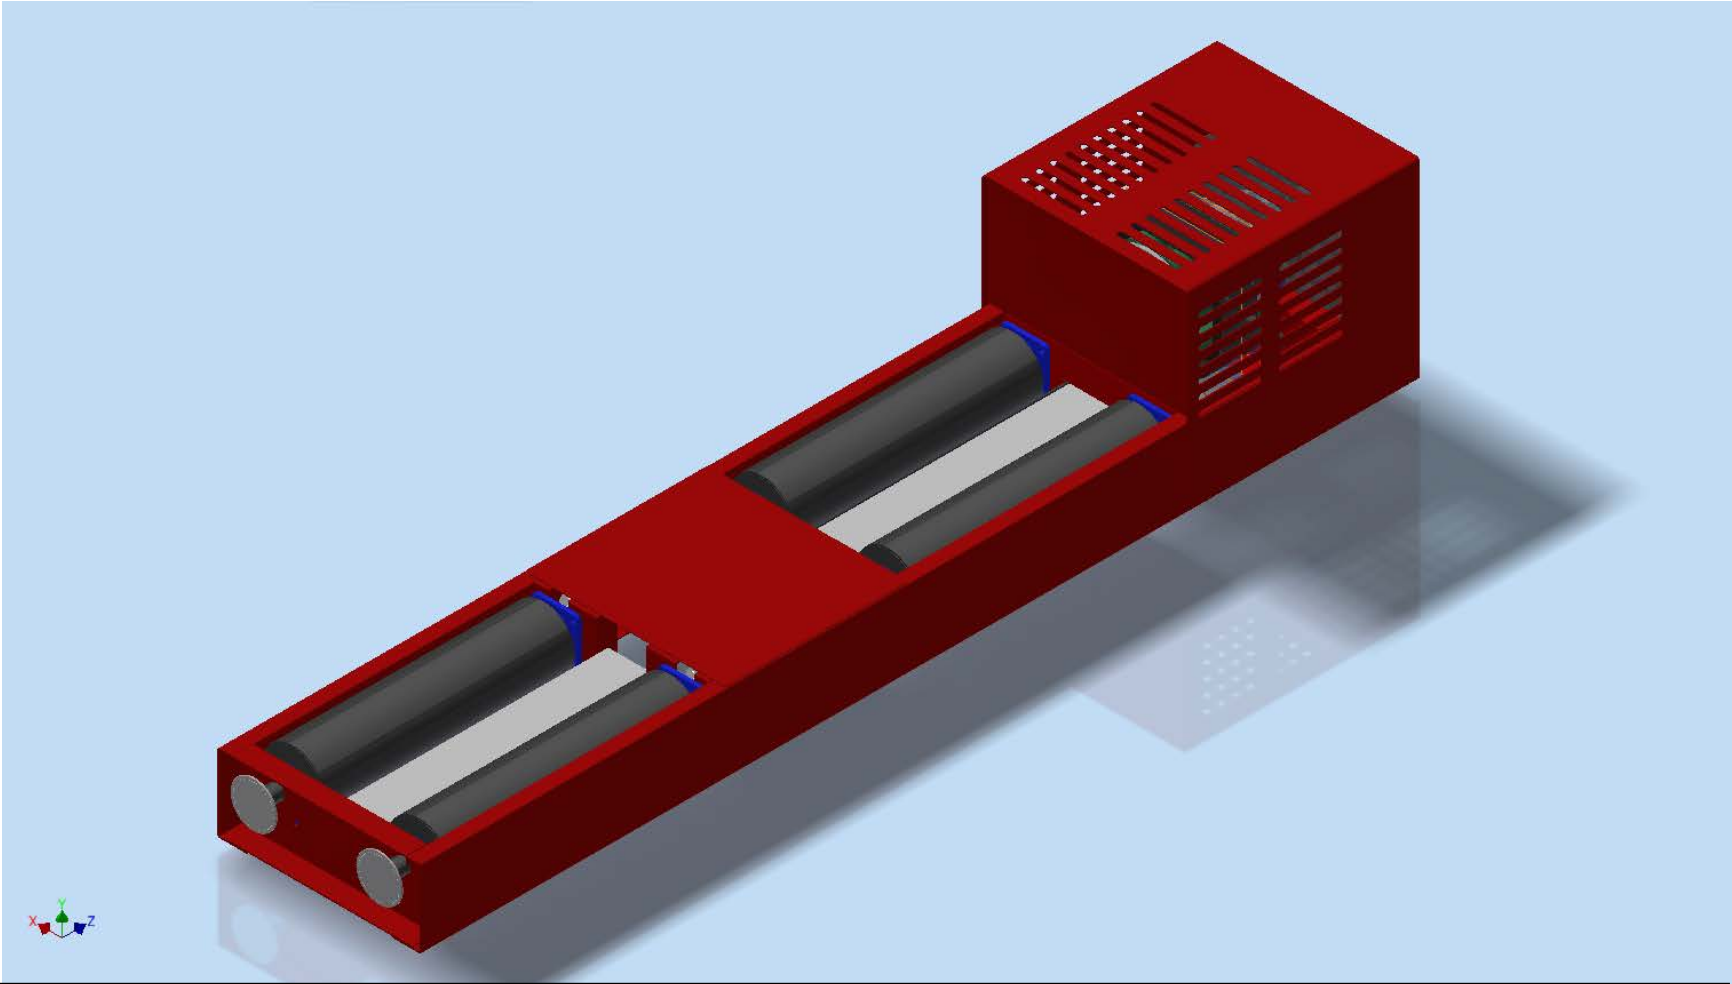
Conjunto del dinamómetro de chasis, perspectiva superior izquierda
